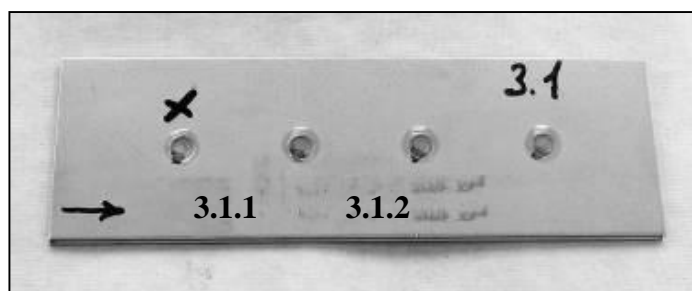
Внешний вид точечной контактной сварки образца № 3.1
